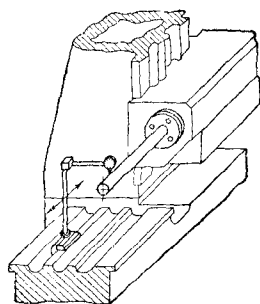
Проверка осей призм поддерживающих кронштейнов изделия у токарного станка для обточки шеек.
